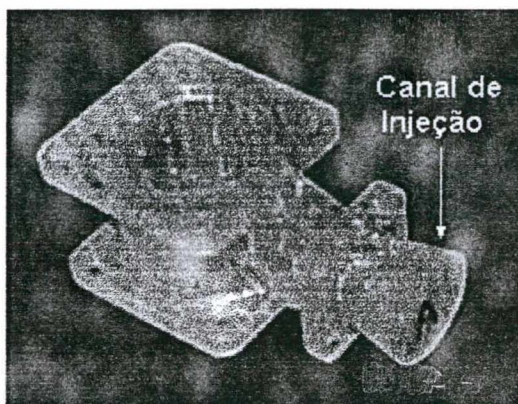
Padrão QuickCast™ pronto para ser enviado para a fundição.
